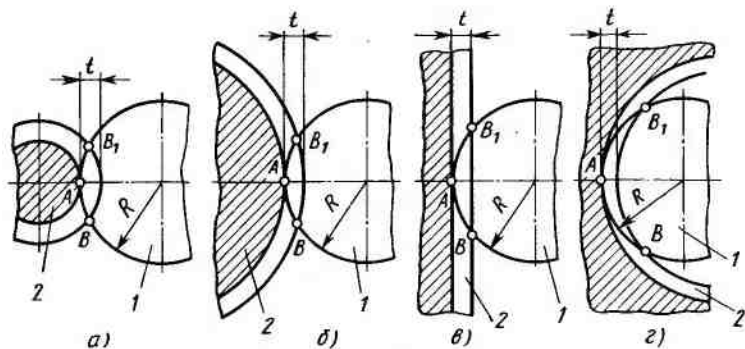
Схема дуги контакта круга с заготовкой при шлифовании:
